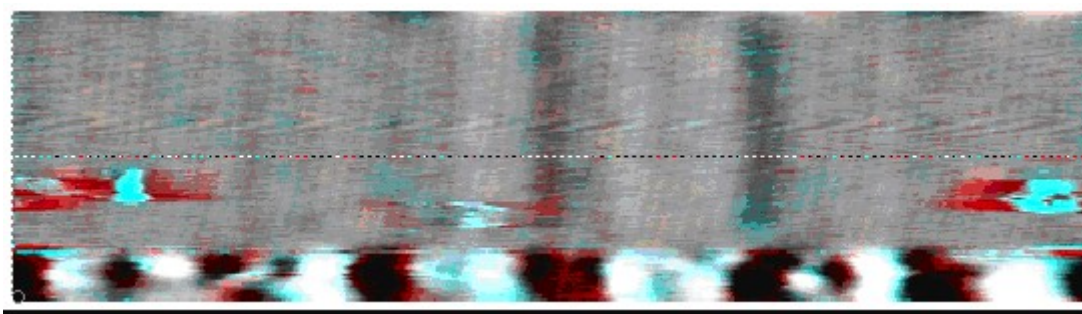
Сканограмма шлифованной цилиндрической поверхности рабочей части вала ротора №35, снятая на вихретоковом приборе ПВК-К2М по линии контроля на 64 обороте, в зоне диаметра шлифованной поверхности
